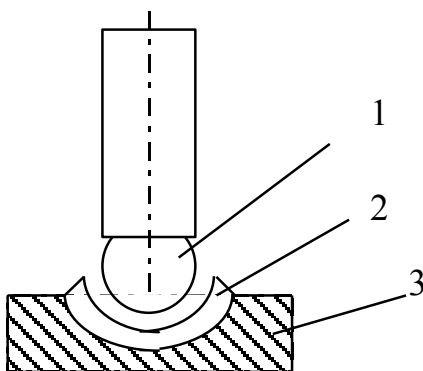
Схема выколотки: 1 - пуансон; 2 - листовая заготовка; 3 наковальня (анка)
